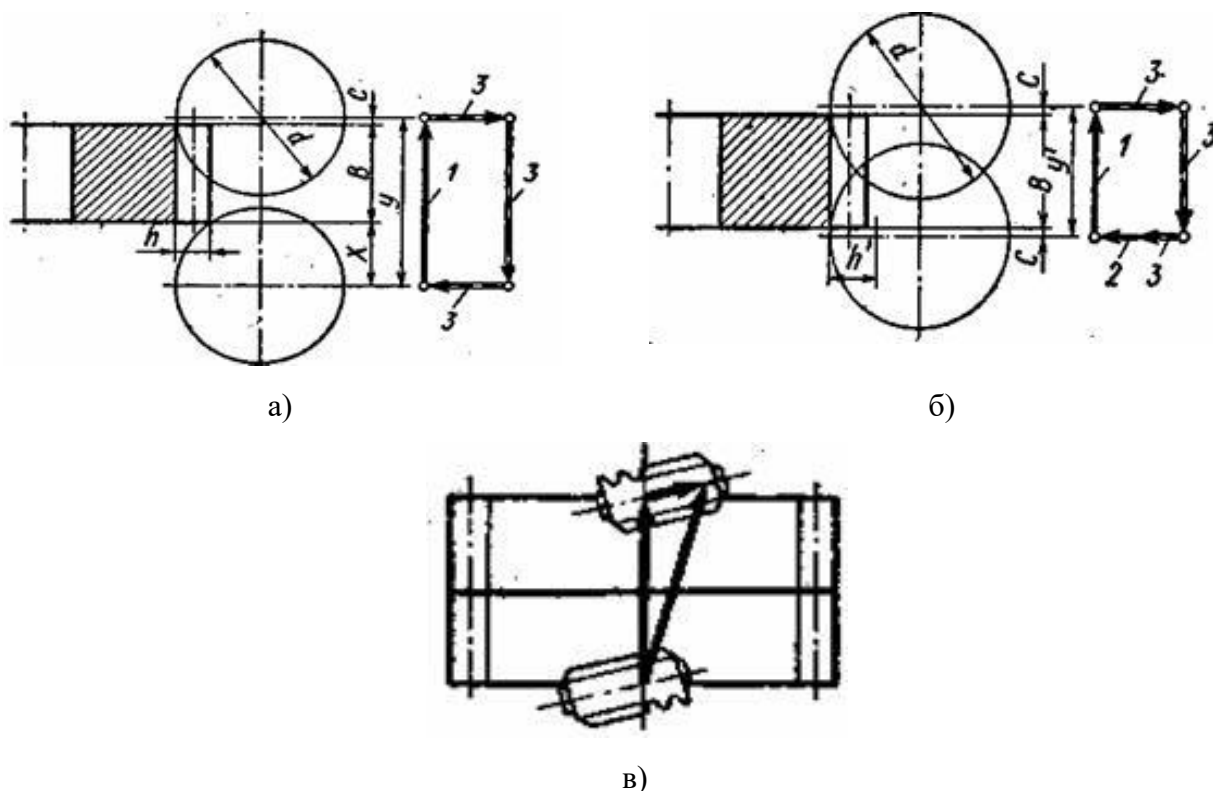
Схемы видов подач при зубофрезеровании:
